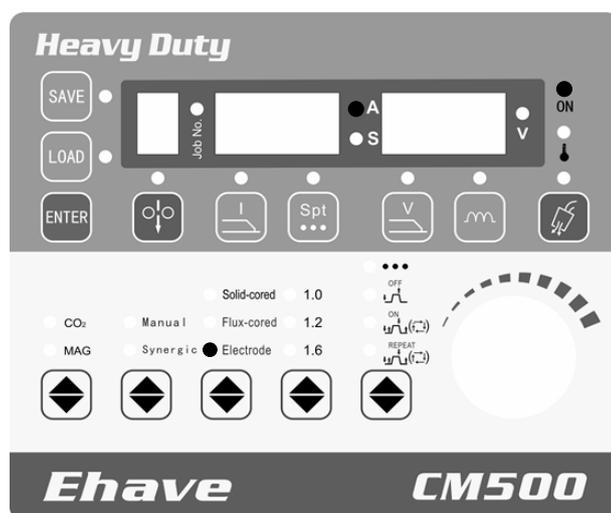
Выбор режима ручной дуговой сварки.
